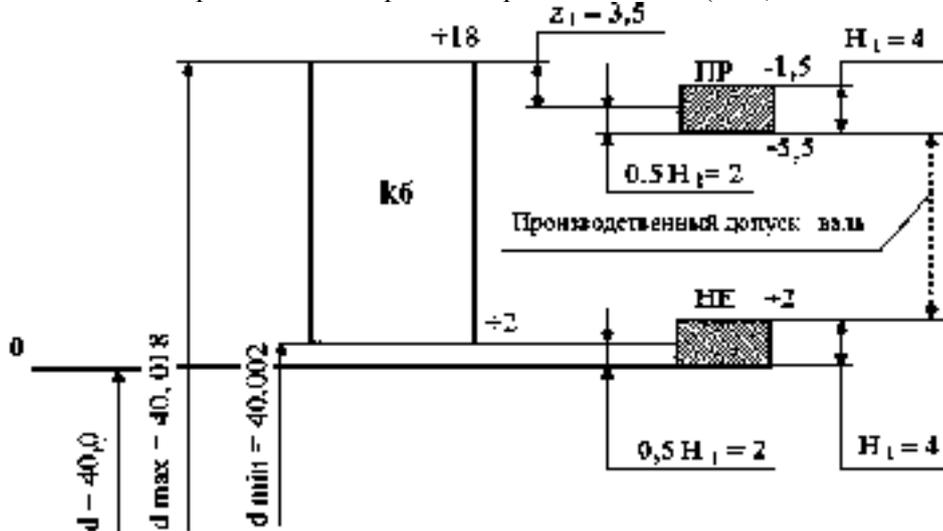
Схема расположения полей допусков на изготовление калибра - скобы для контроля вала $\varnothing 40 k6^{(+0,018)}$
